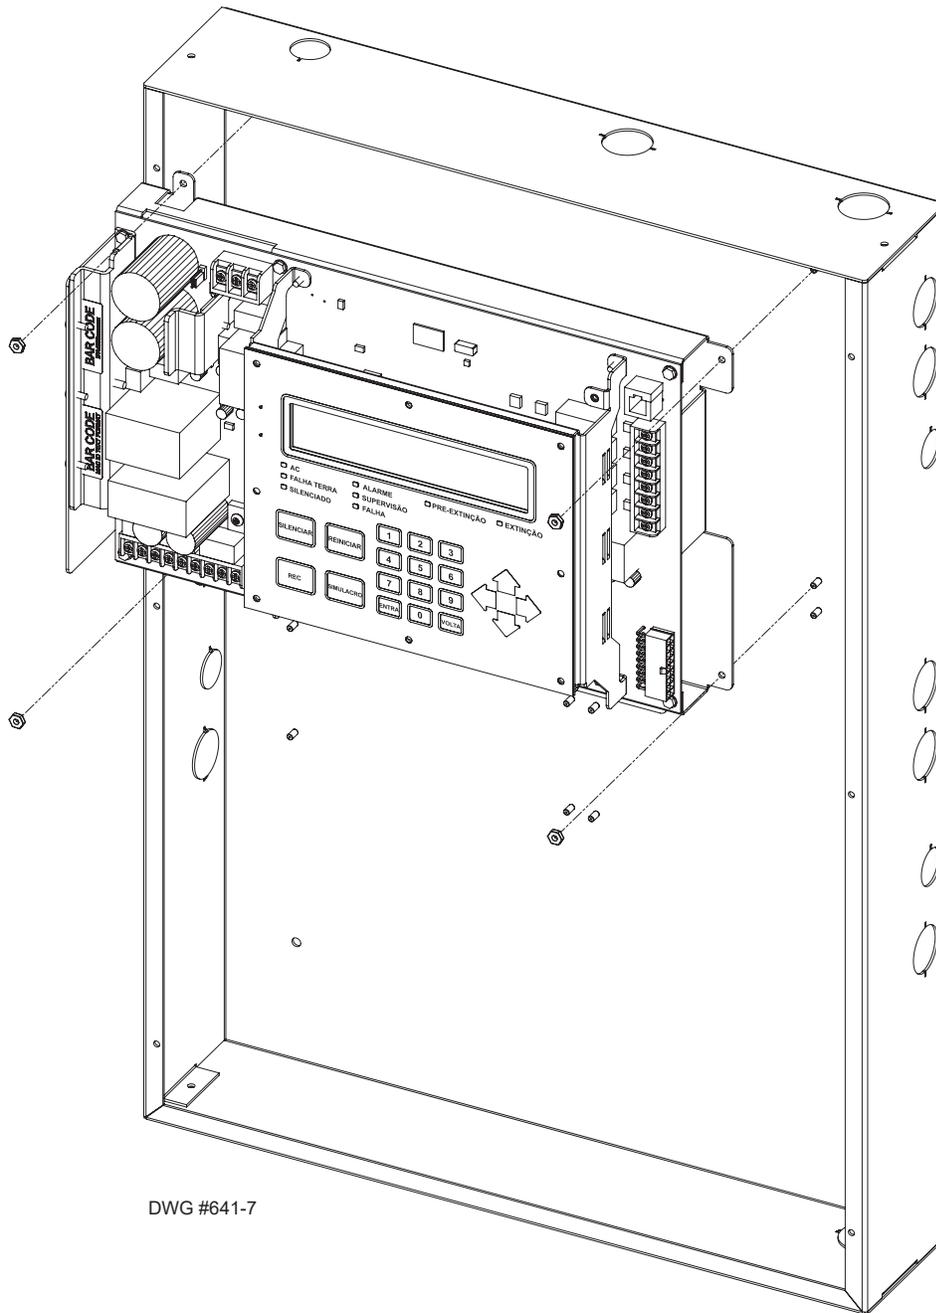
Gabinete do IPA-4000 Mostrando Conjunto da Placa Eletrônica
